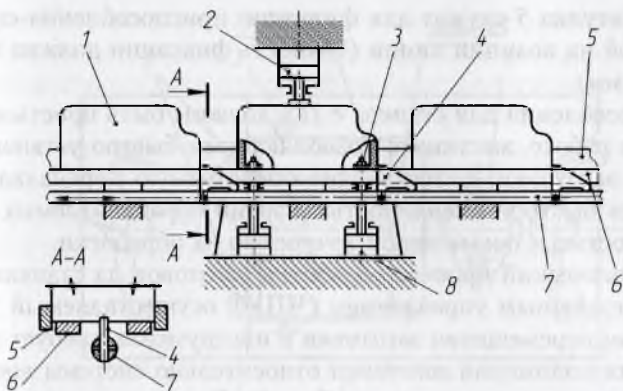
Приспособление для установки и перемещения обрабатываемых заготовок на АЛ
